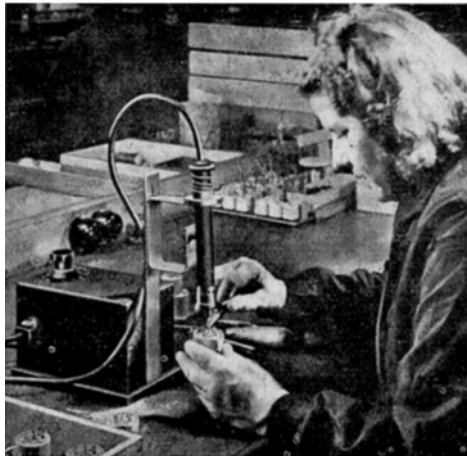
Für die Massenfertigung läßt sich der Schweißgriffel in einen an das Netzgerät angebaute Halter einspannen.
